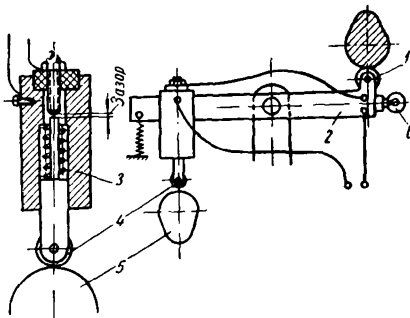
Схема измерения припуска на обработку по криволинейной поверхности поковки: 1 — ролик, обкатывающий поверхность поковки; 2 — равноплечий рычаг; 3 — электроконтактный глубиномер; 4 — ролик, обкатывающий эталон; 5 — эталон, вращающийся синхронно с поковкой; 6 — сигнальная лампочка (загорается при недостатке припуска)
